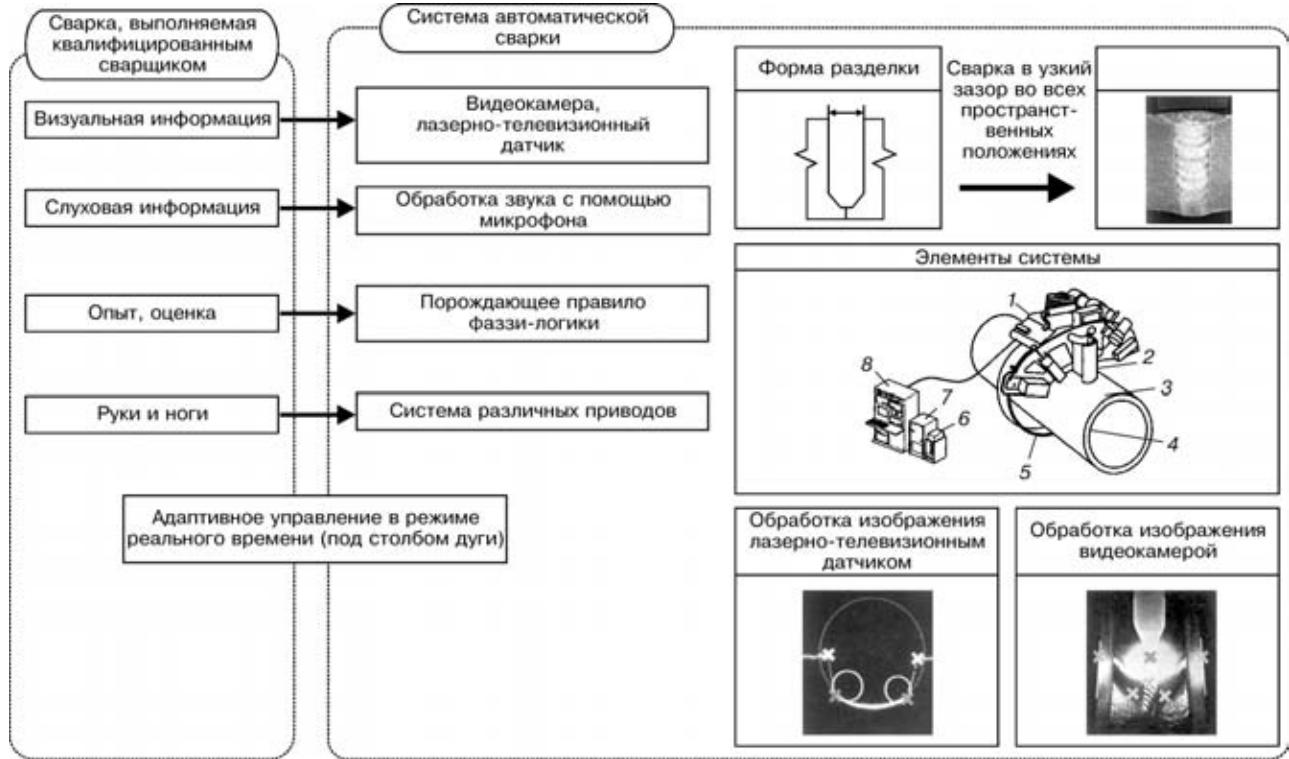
Концепция процесса сварки во всех пространственных положениях (1 – сварочная головка; 2 – видеокамера; 3 – лазерно-телеизионный датчик; 4 – труба; 5 – направляющий рельс; 6 – система охлаждающей воды; 7 – источник питания; 8 – система управления сваркой)
